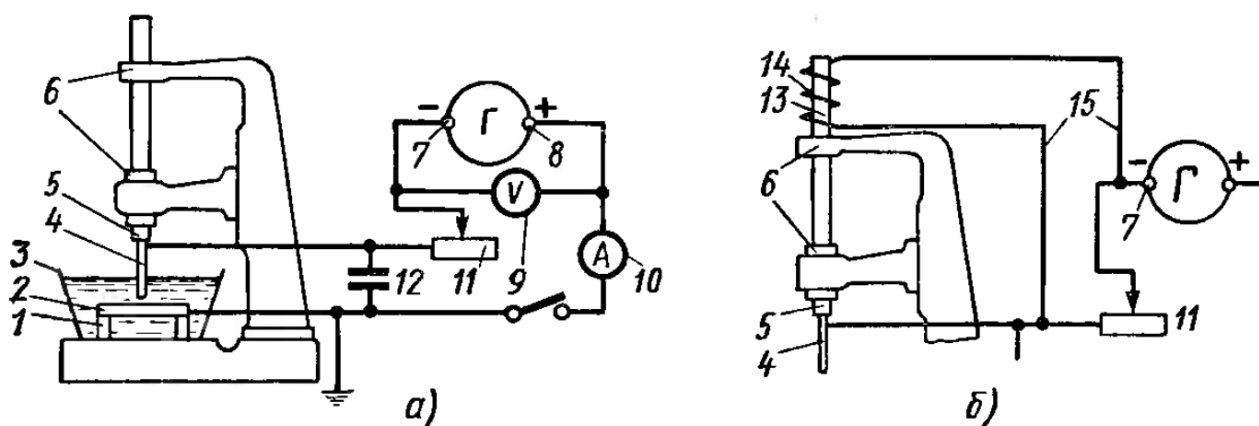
Верстат для електроіскрової прошивки (а), та соленоїдний редуктор (б).
